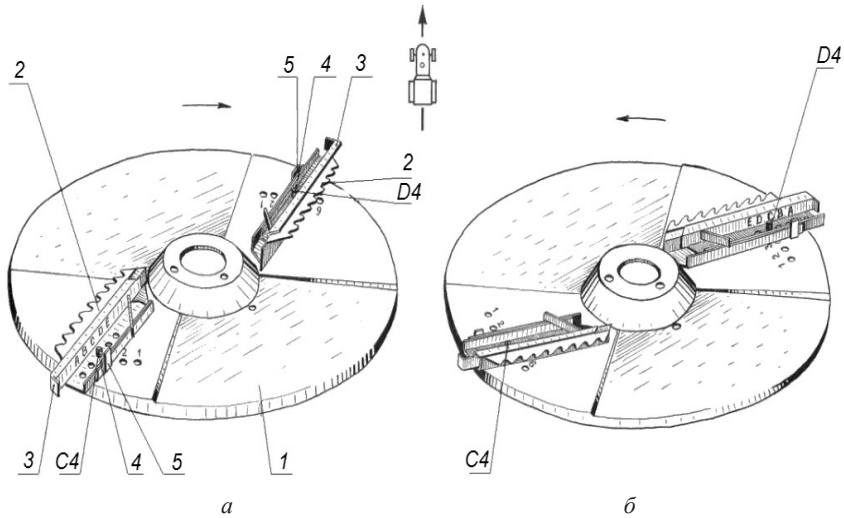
Дисковые метатели: *а* – левый метатель; *б* – правый метатель; 1 – диск; 2 – направляющая; 3 – лопатка; 4 – фиксатор; 5 – упор
